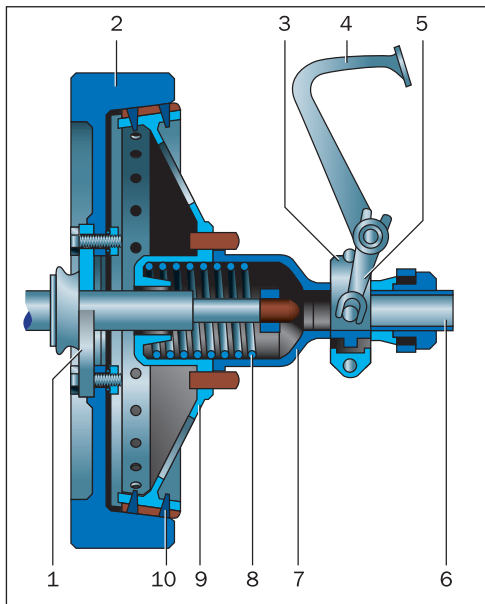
Сцепление конусного типа: 1 — фланец коленчатого вала; 2 — маховик; 3 — муфта выключения сцепления; 4 — педаль сцепления; 5 — рычаг выключения сцепления; 6 — вал сцепления; 7 — кожух сцепления; 8 — пружина; 9 — конус сцепления; 10 — фрикционная накладка
